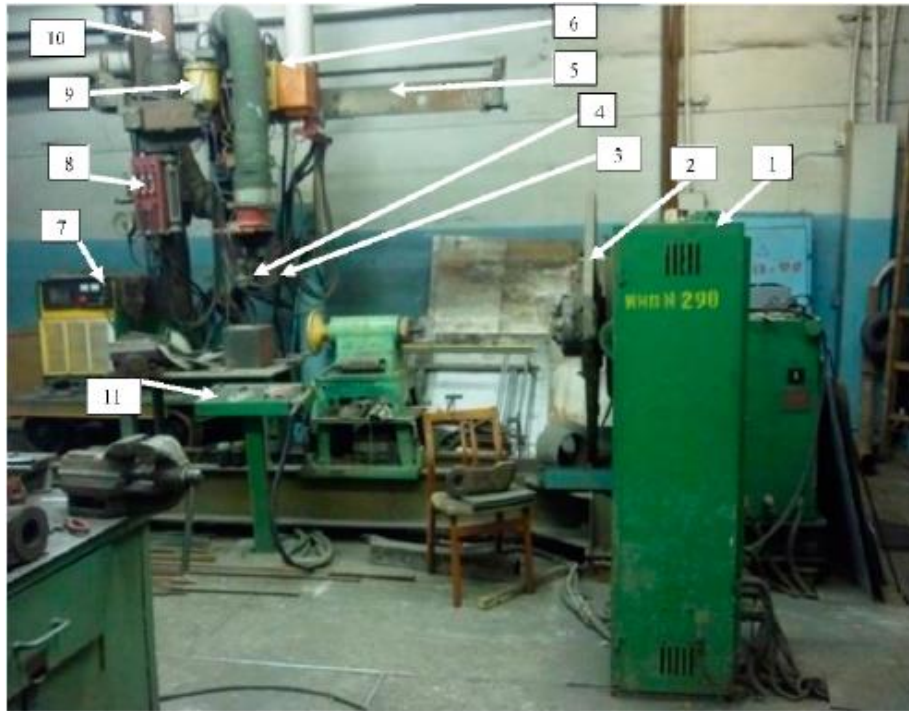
Установка УПН-303: 1 – шафа управління; 2 – маніпулятор; 3 – механізм поперечних коливань; 4 – плазматрон; 5 – напрямна балка; 6 – привід плазматрона; 7 – джерело живлення; 8 – регулятори витрати газів; 9 – порошковий живильник; 10 – підйомно-поворотна колона, 11 – пульт управління.
